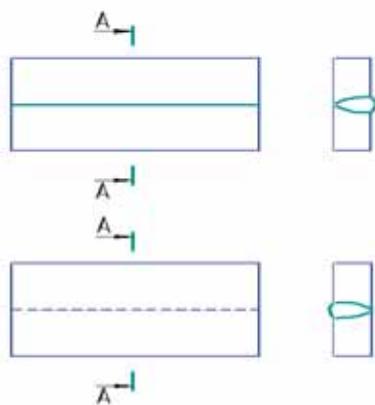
Изображение сварных швов на чертежах
